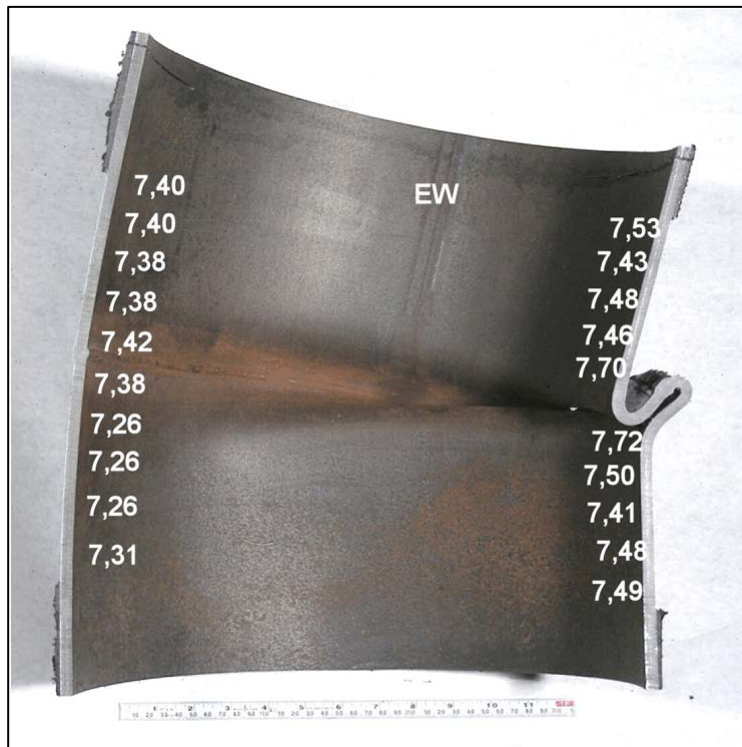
Junta 084/83, vista de la sección del doblez, anotado con las mediciones de espesores de pared en milímetros, y la posición de un EW (Electric Weld). (Fuente: Informe Laboratorio de Stork)
